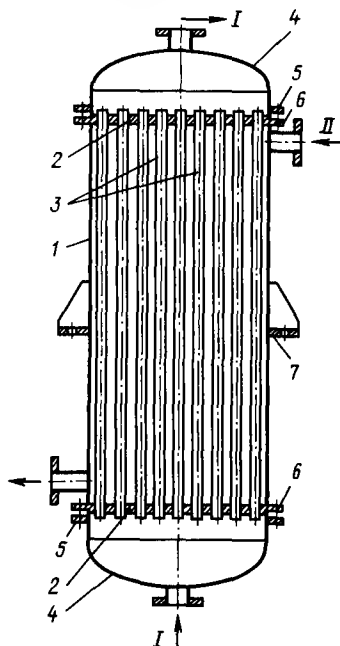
Кожухотрубчатый теплообменный аппарат одноходовой непрерывного действия: 1 — корпус или кожух; 2 — трубные решетки; 3 — трубы; 4 — днища и крышки распределительных камер; 5, 6 — фланцы; 7 — опоры
